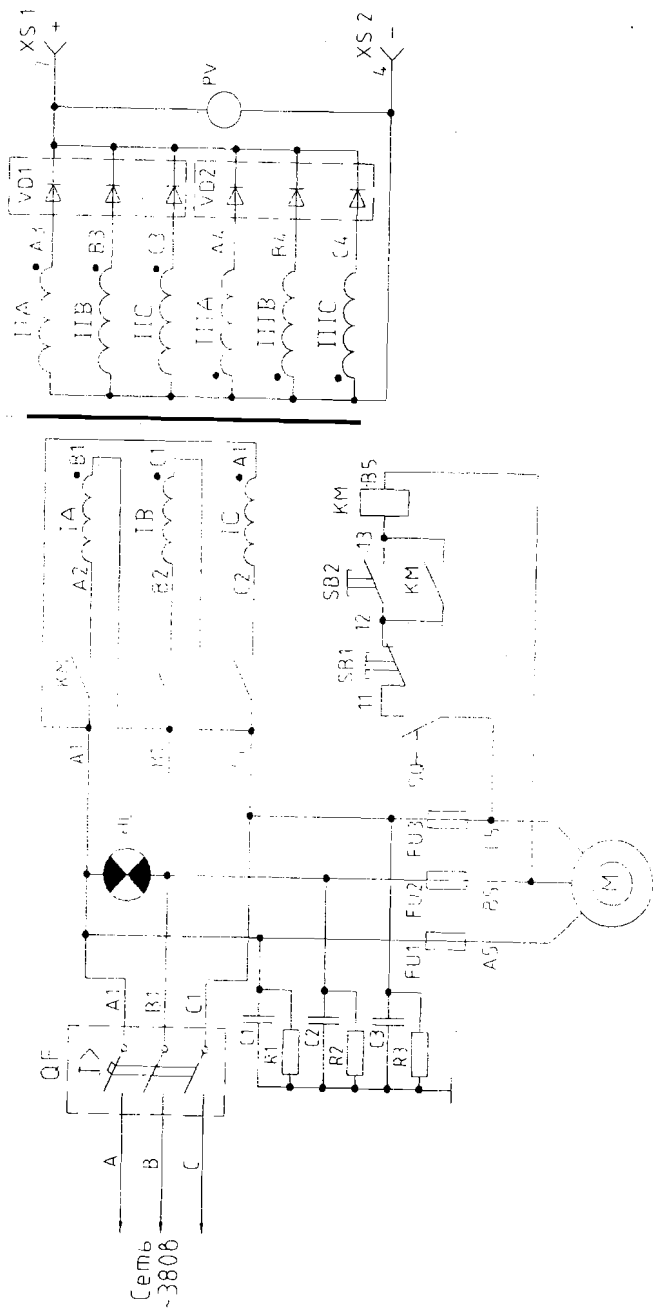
Схема электрической цепи сварочного выпрямителя ВДМ1201 и ВДМ1601
